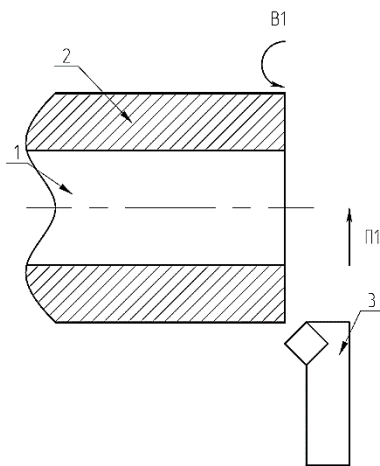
Схема точения торца заготовки при перемещении резца снаружи к оси заготовки
